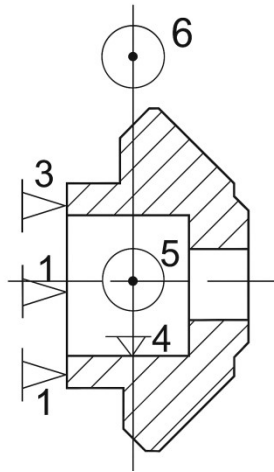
Базування заготовки при обробці торця з боку конуса
